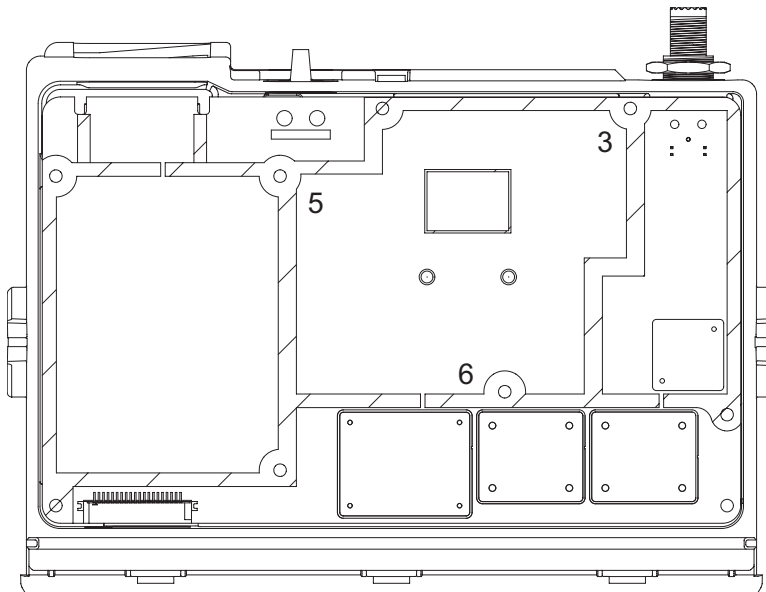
Sequência do Parafuso para Comprimir a PCB
